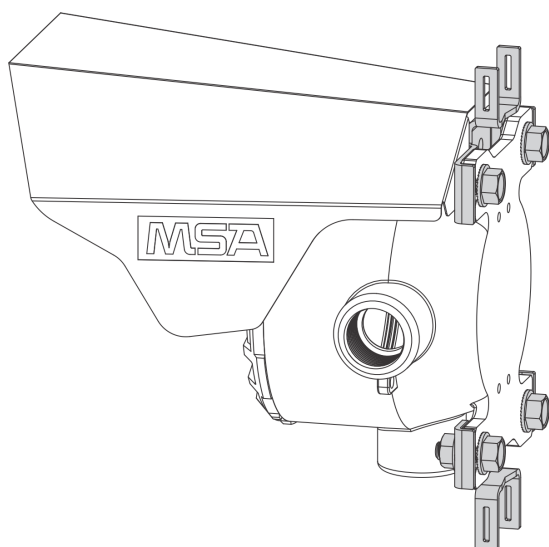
Солнцезащитное устройство с универсальным креплением на трубу
